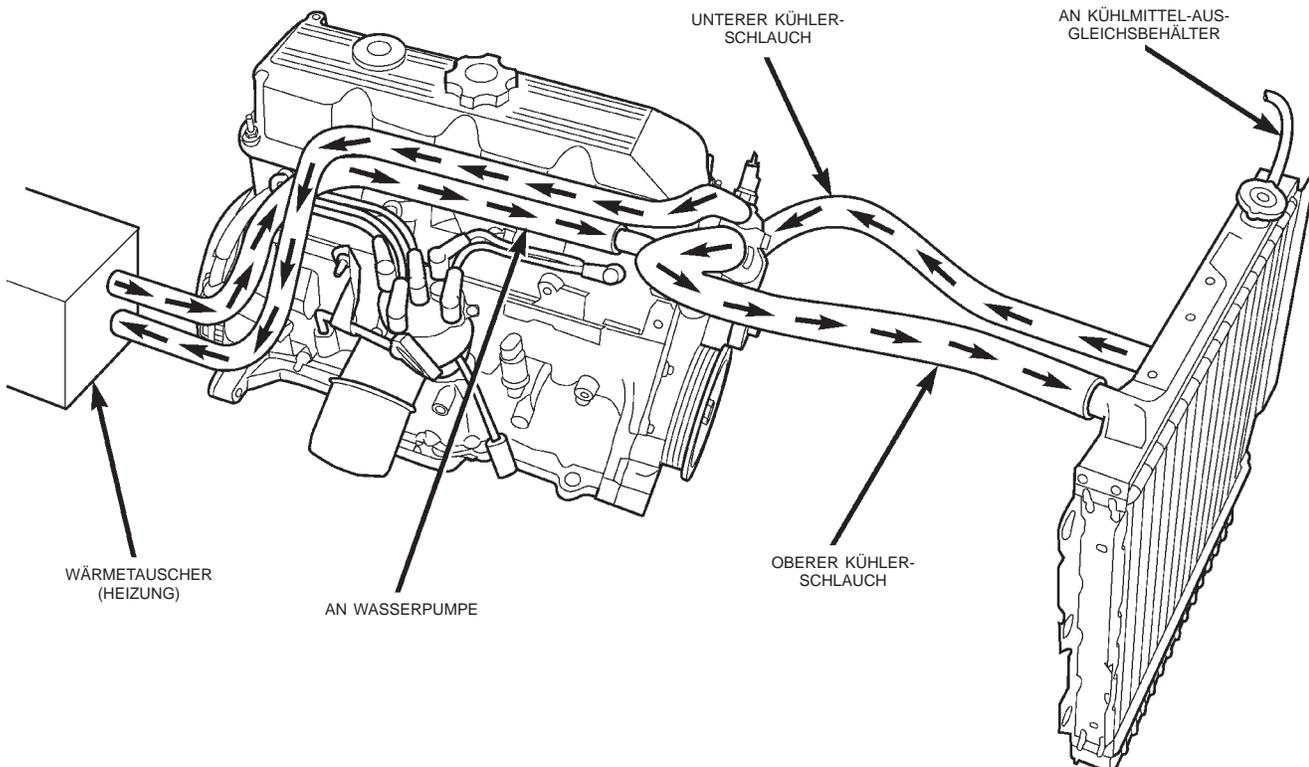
Kühlmittelkreislauf—2.5L-Motor
